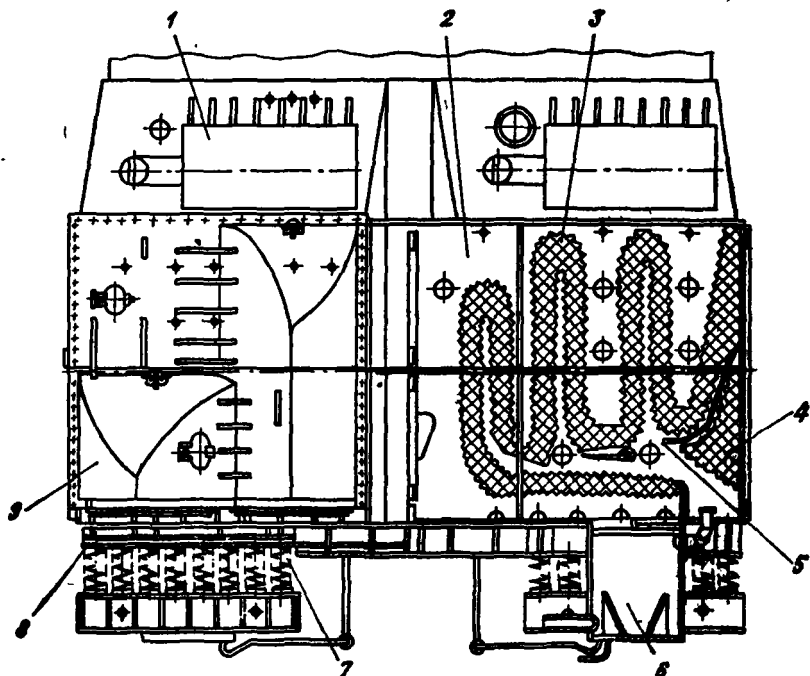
Подвальный конденсатор турбоустановки К-300-240-2:
